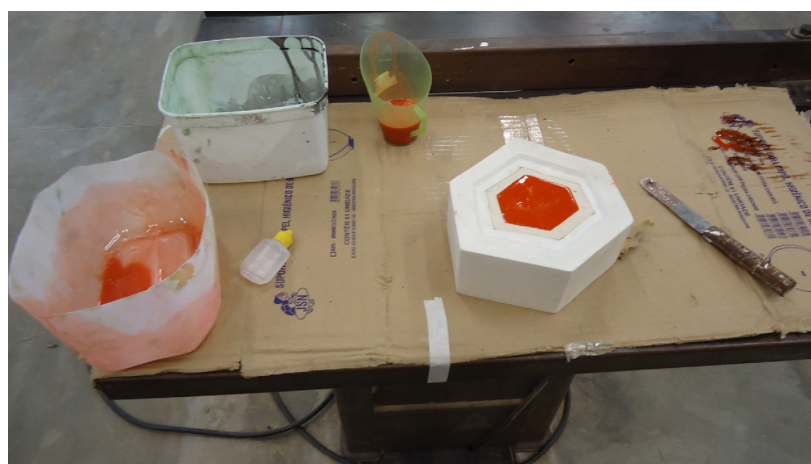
Fundição do módulo 1 em resina de poliéster com pigmentação opaca sobre mesa vibratória improvisada.
